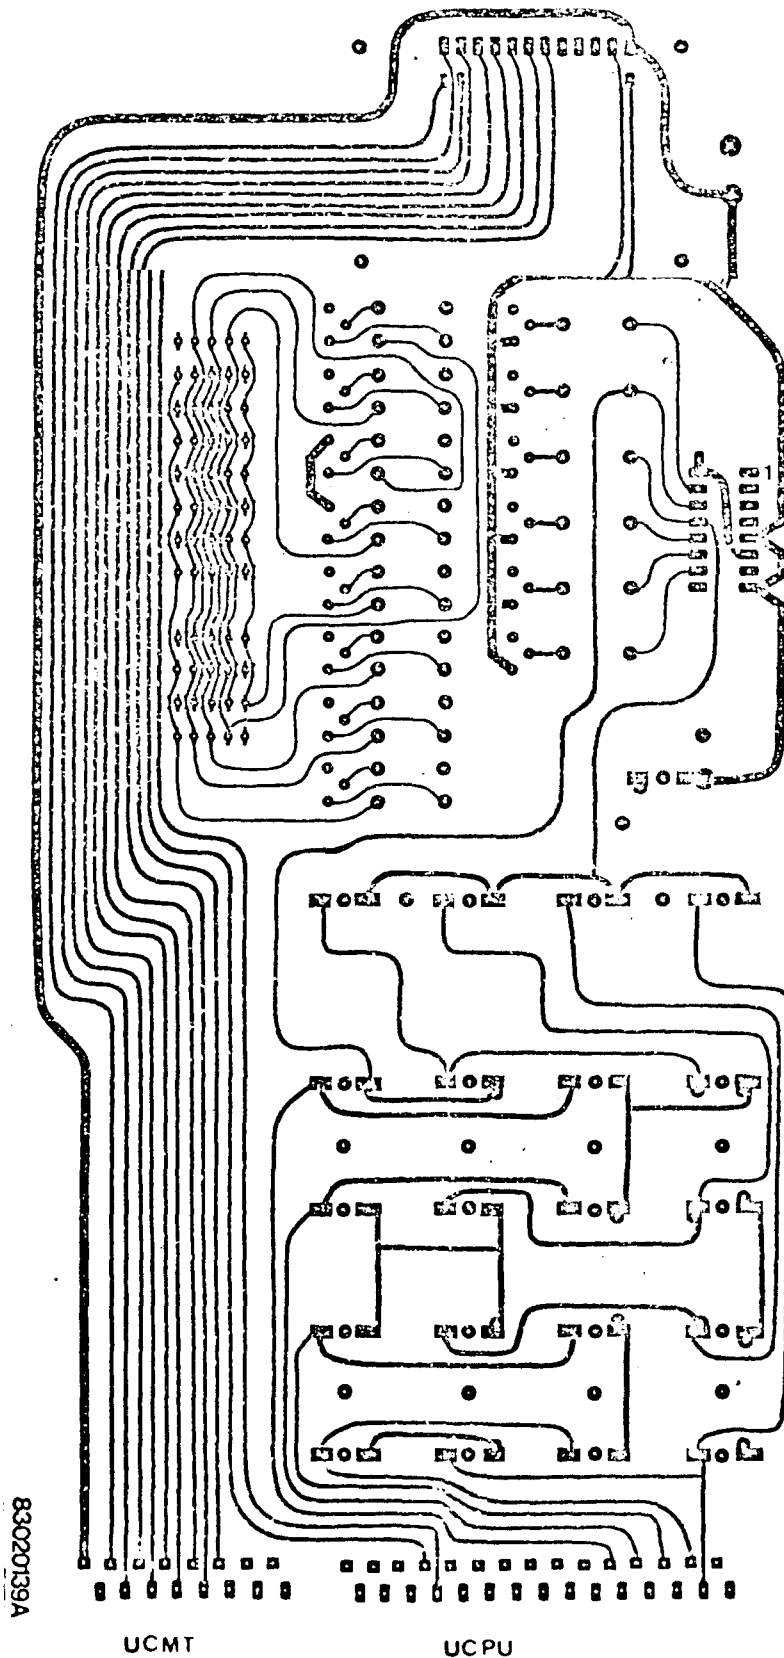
LAY-OUT DA PLACA DO PAÍNEL FRONTAL
